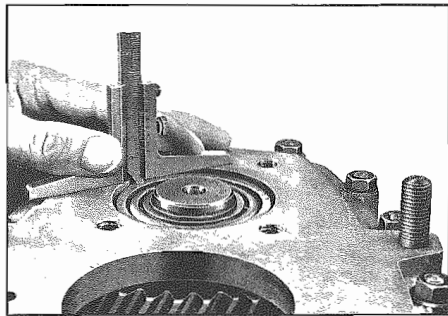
Misurazione del gioco tra l'anello esterno del cuscinetto e la parte frontale della scatola - Measuring gap between bearing outer race and face end of housing
